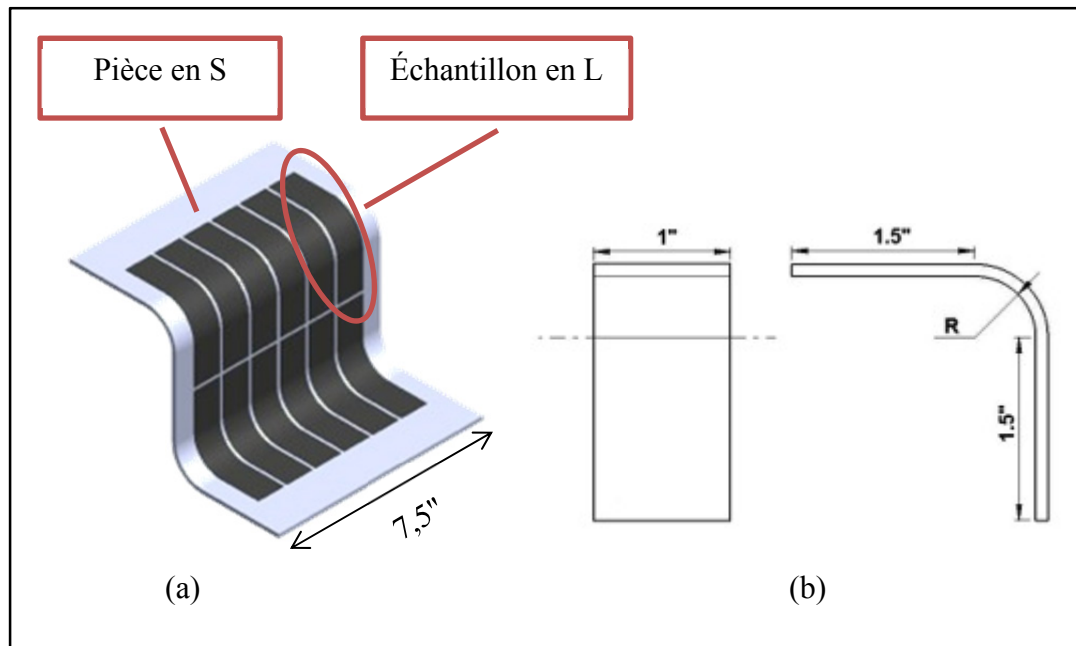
Emplacement (a) et dimensions (b) des échantillons extraits des pièces estampées avec les moules M1 et M2
